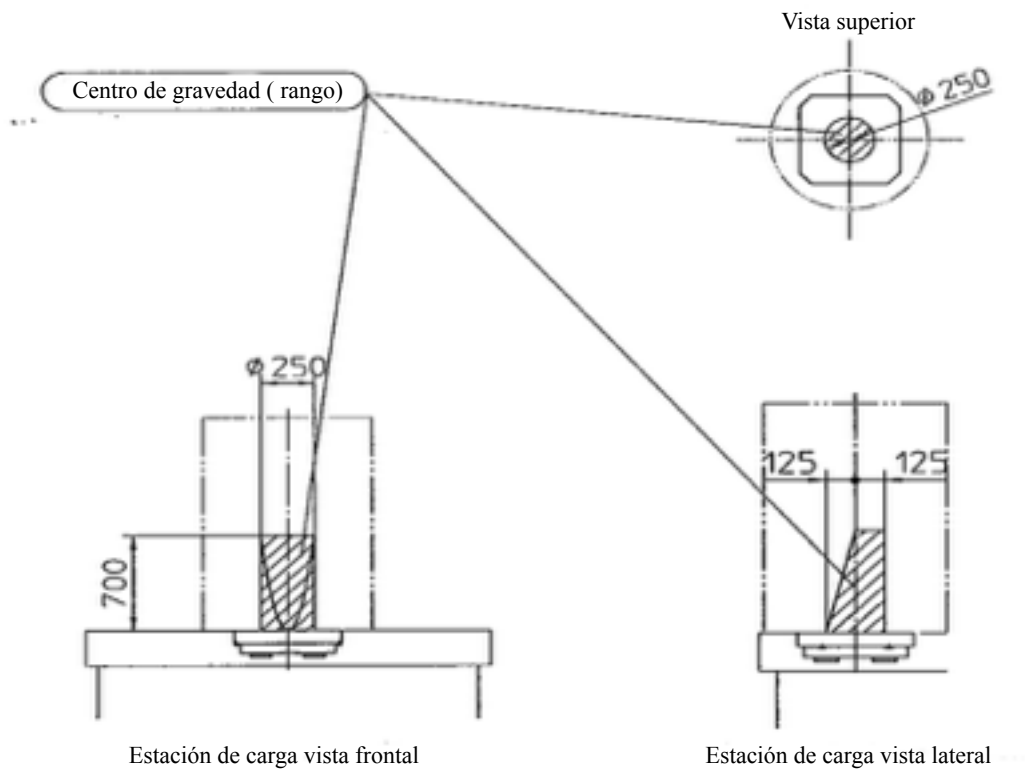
Restricciones de la pieza de trabajo (a61/a71)
